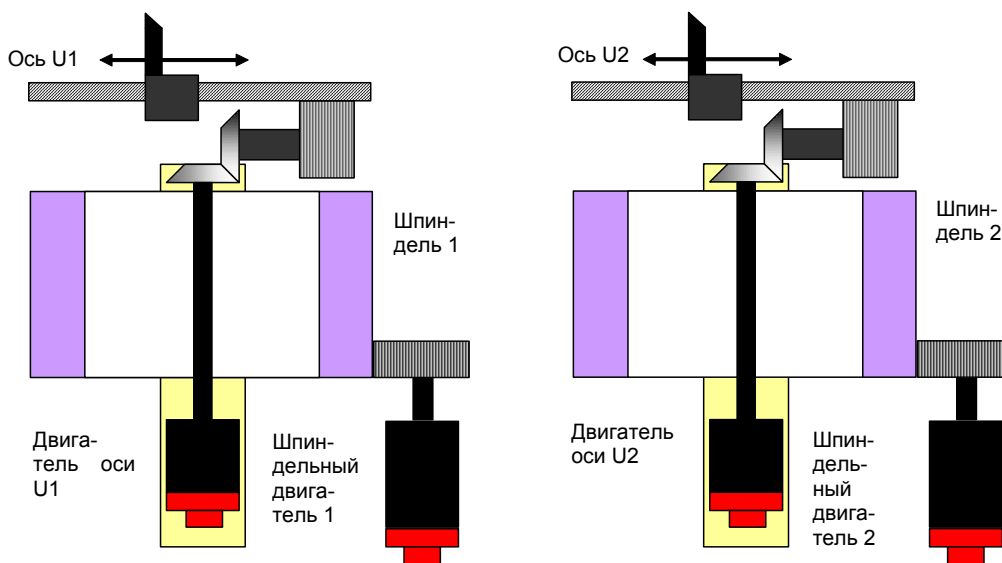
(b) Пример конструкции станка с двумя осями U
